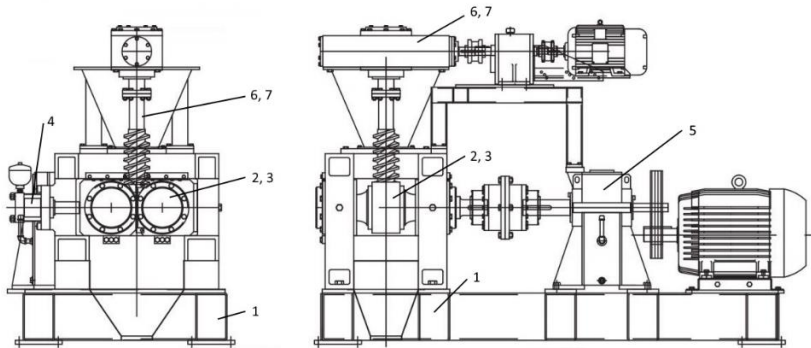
Валковий прес принципова конструктивна схема: 1 – рама преса; 2 – валки; 3 – змінні бандажі валків; 4 – гідравлічний пристрій захисту валків від перевантаження; 5 – лінія приводу преса; 6 – підпресовник шнекового типу; 7 – завантажувальний пристрій.
